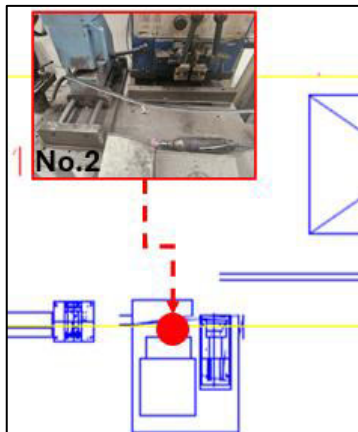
Fuente de suciedad No.2 soldador
